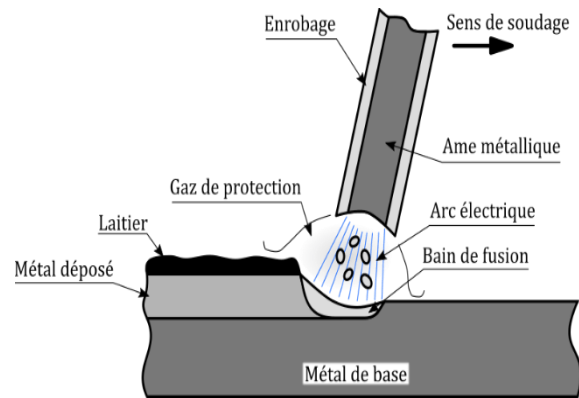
Schéma d'assemblage par soudage.
